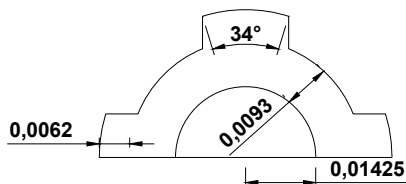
Dimensões físicas do rotor do MRC projetado.
